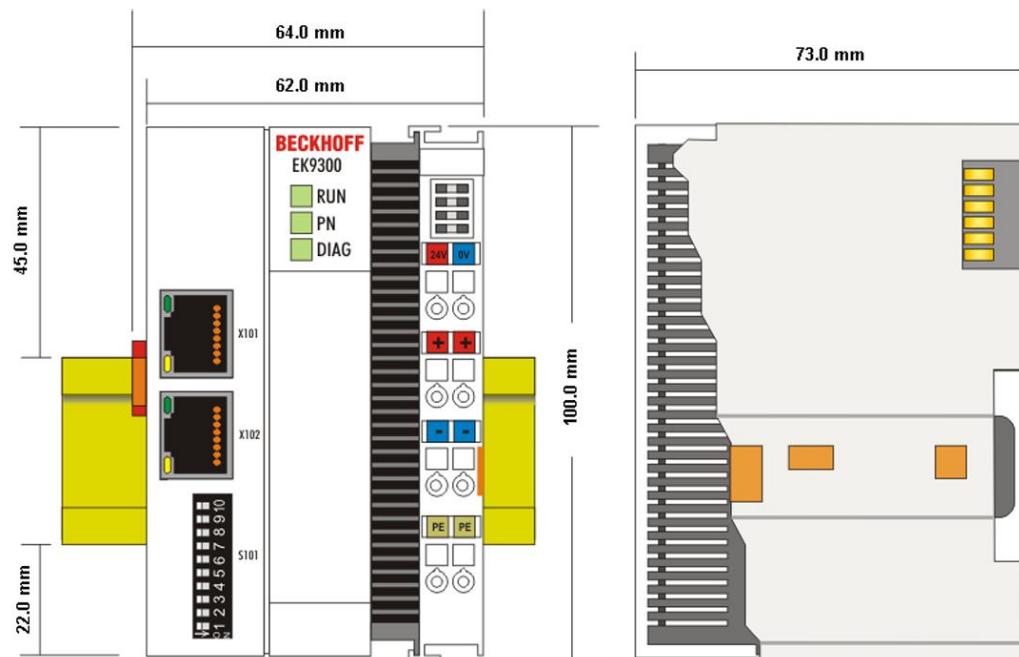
Dimensiones del acoplador de bus EK9300⁷⁸.
